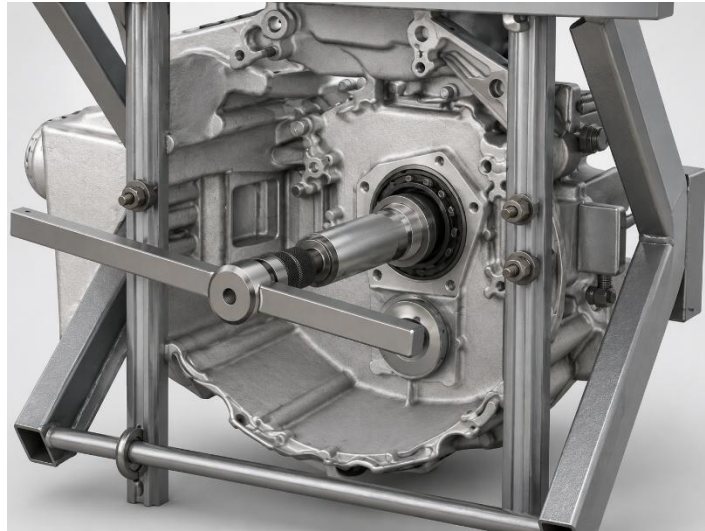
Відкручування корончатої гайки з кінцевої частини первинного вала.
